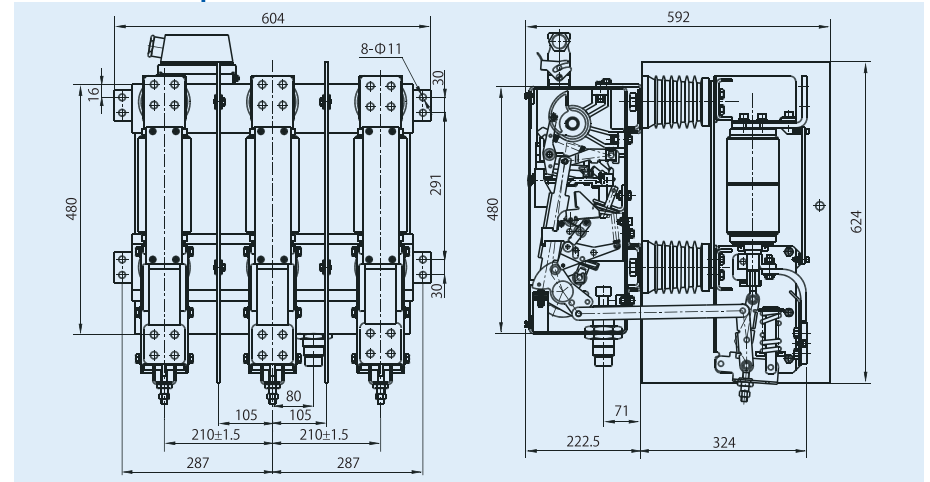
Внешний вид и монтажные размеры выключателя стационарного исполнения серии ZN65B-12
